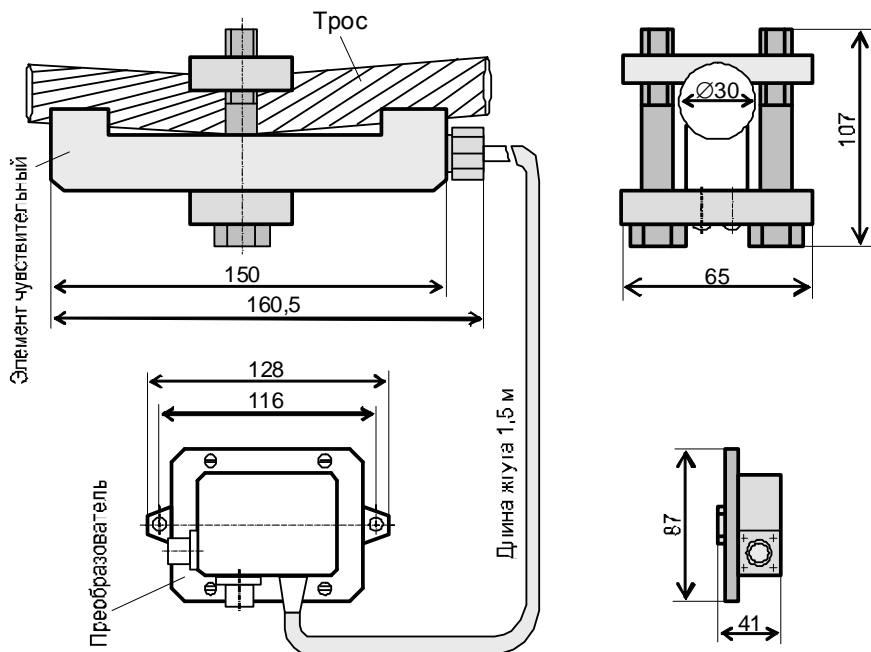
Габаритные и присоединительные размеры ДУКЦ
